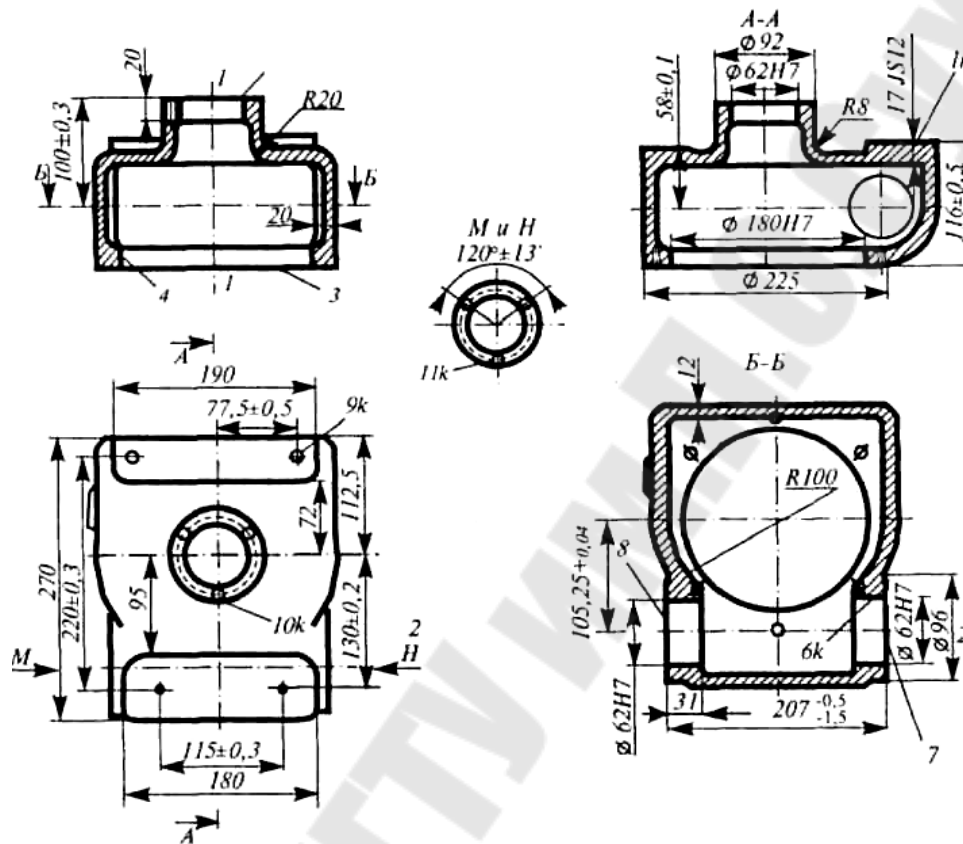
Эскиз корпусной детали с технологической разметкой поверхностей
